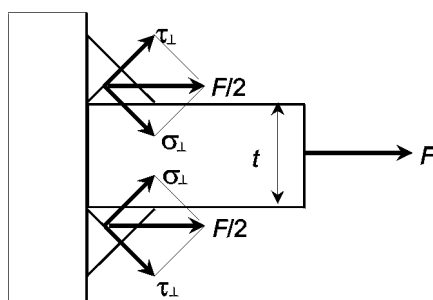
Unión con doble soldadura en ángulo cargada perpendicularmente al eje de soldadura
